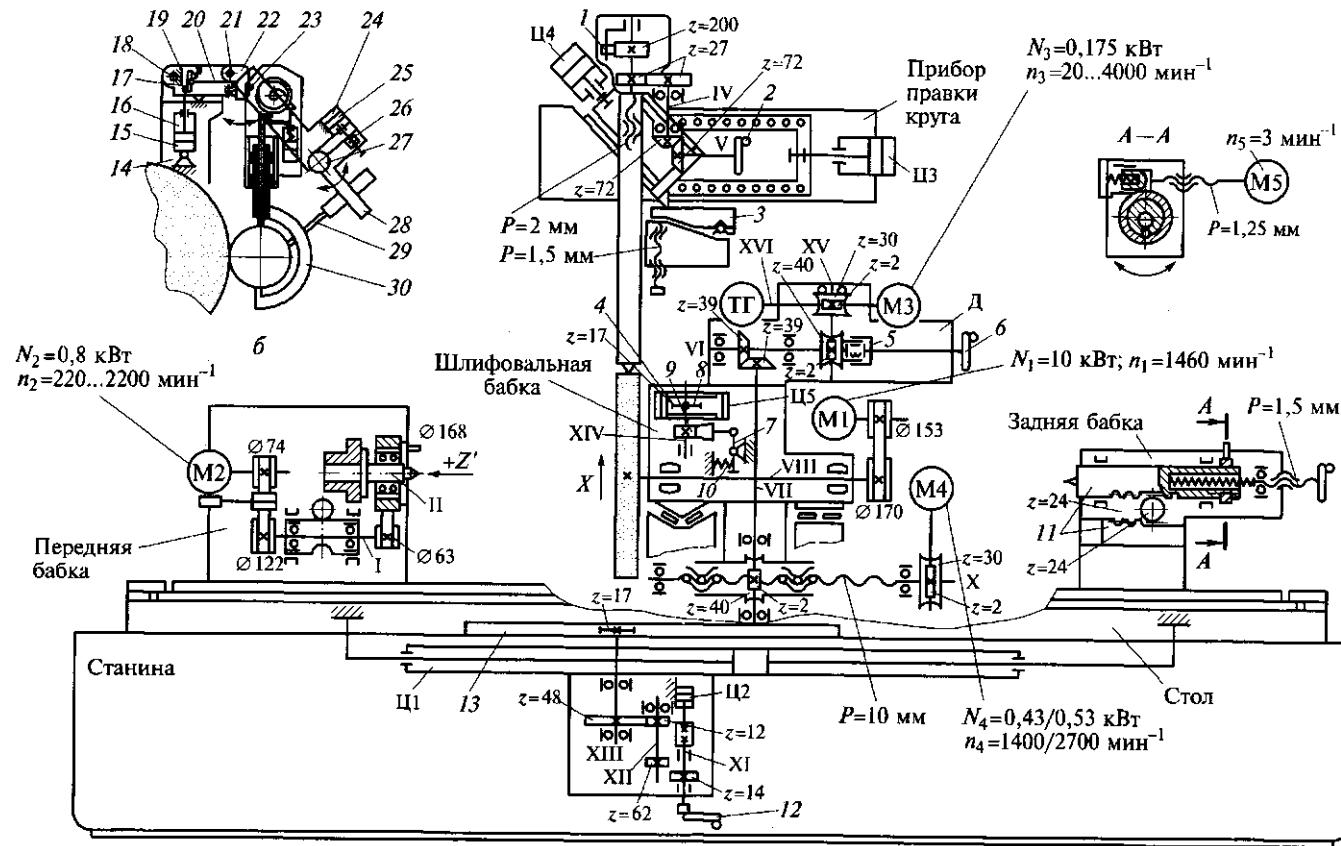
Кинематическая схема круглошлифовального станка с ЧПУ (а) и схема механизмов ввода измерительной скобы и прибора осевой ориентации (б):
